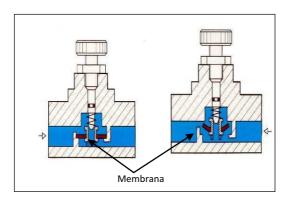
Válvula de estrangulamiento con anti retorno. 38
